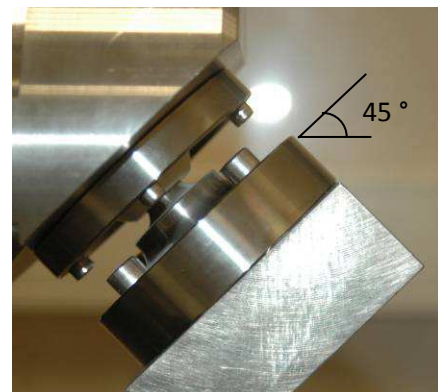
Machine de chocs. Vue de l'ensemble tête et cupule incliné de 45° par rapport à l'horizontale.
